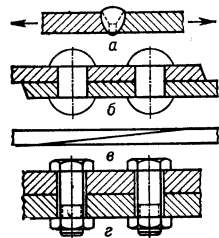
Соединения: а — сварное; б — заклёпочное; в — клеевое; г — резьбовое.
